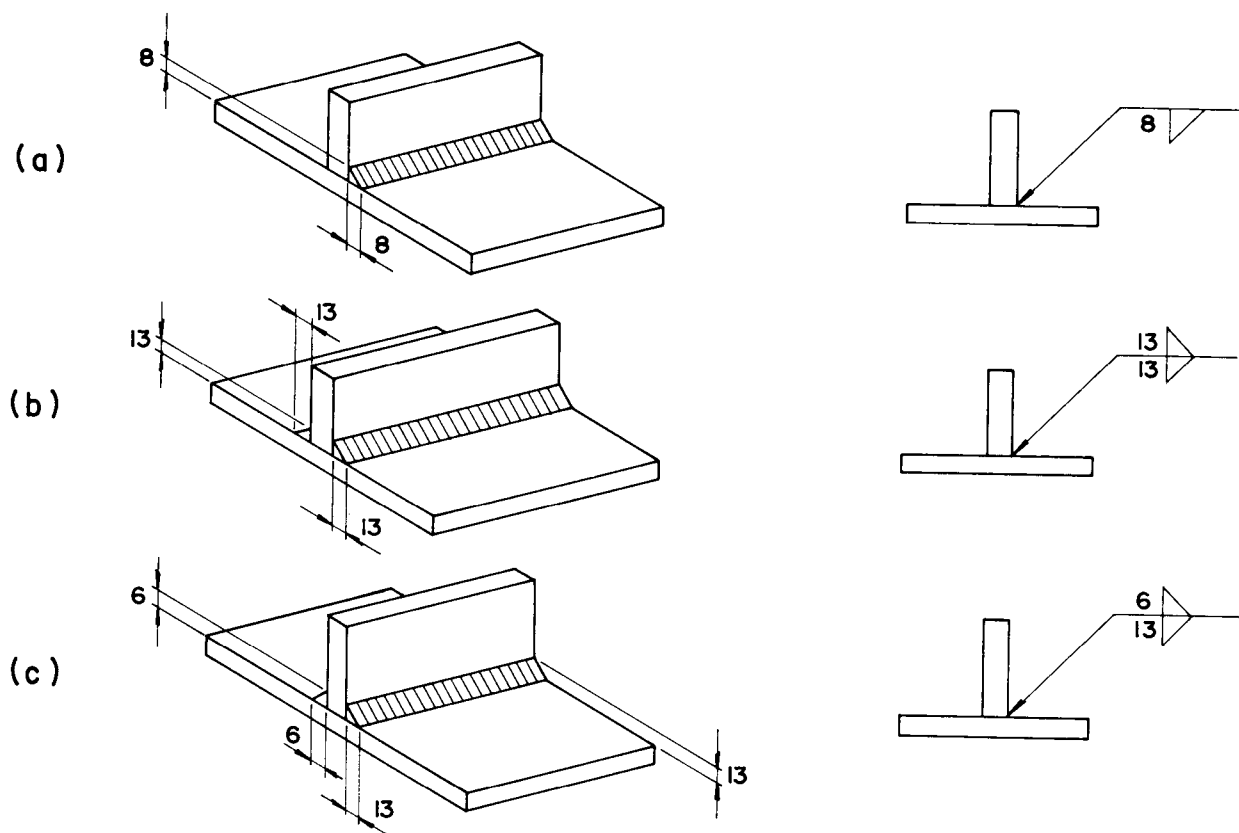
Exemplos de símbolos de soldagem contínua
